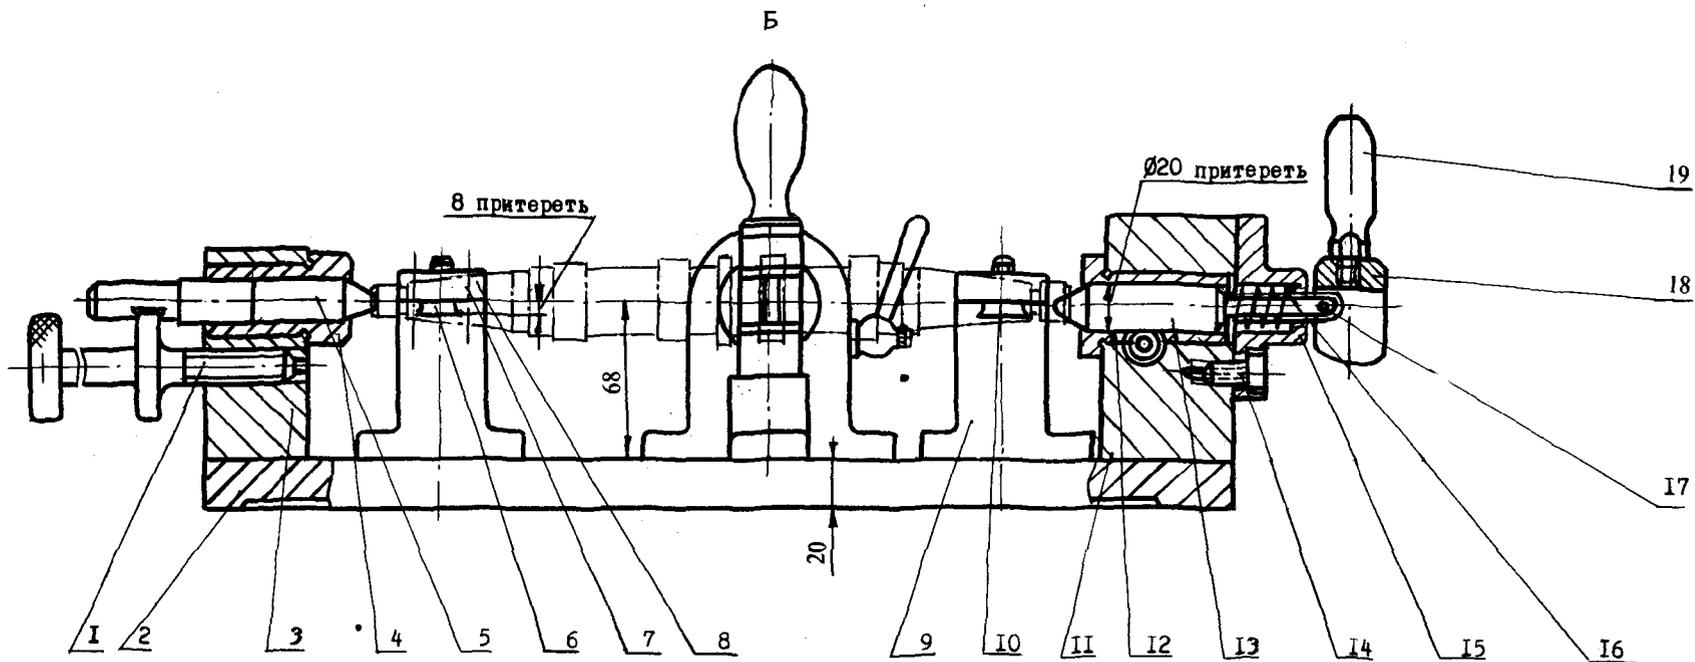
Приспособление для контроля смещения шпоночных канавок (вид Б на рис. 3.12):
